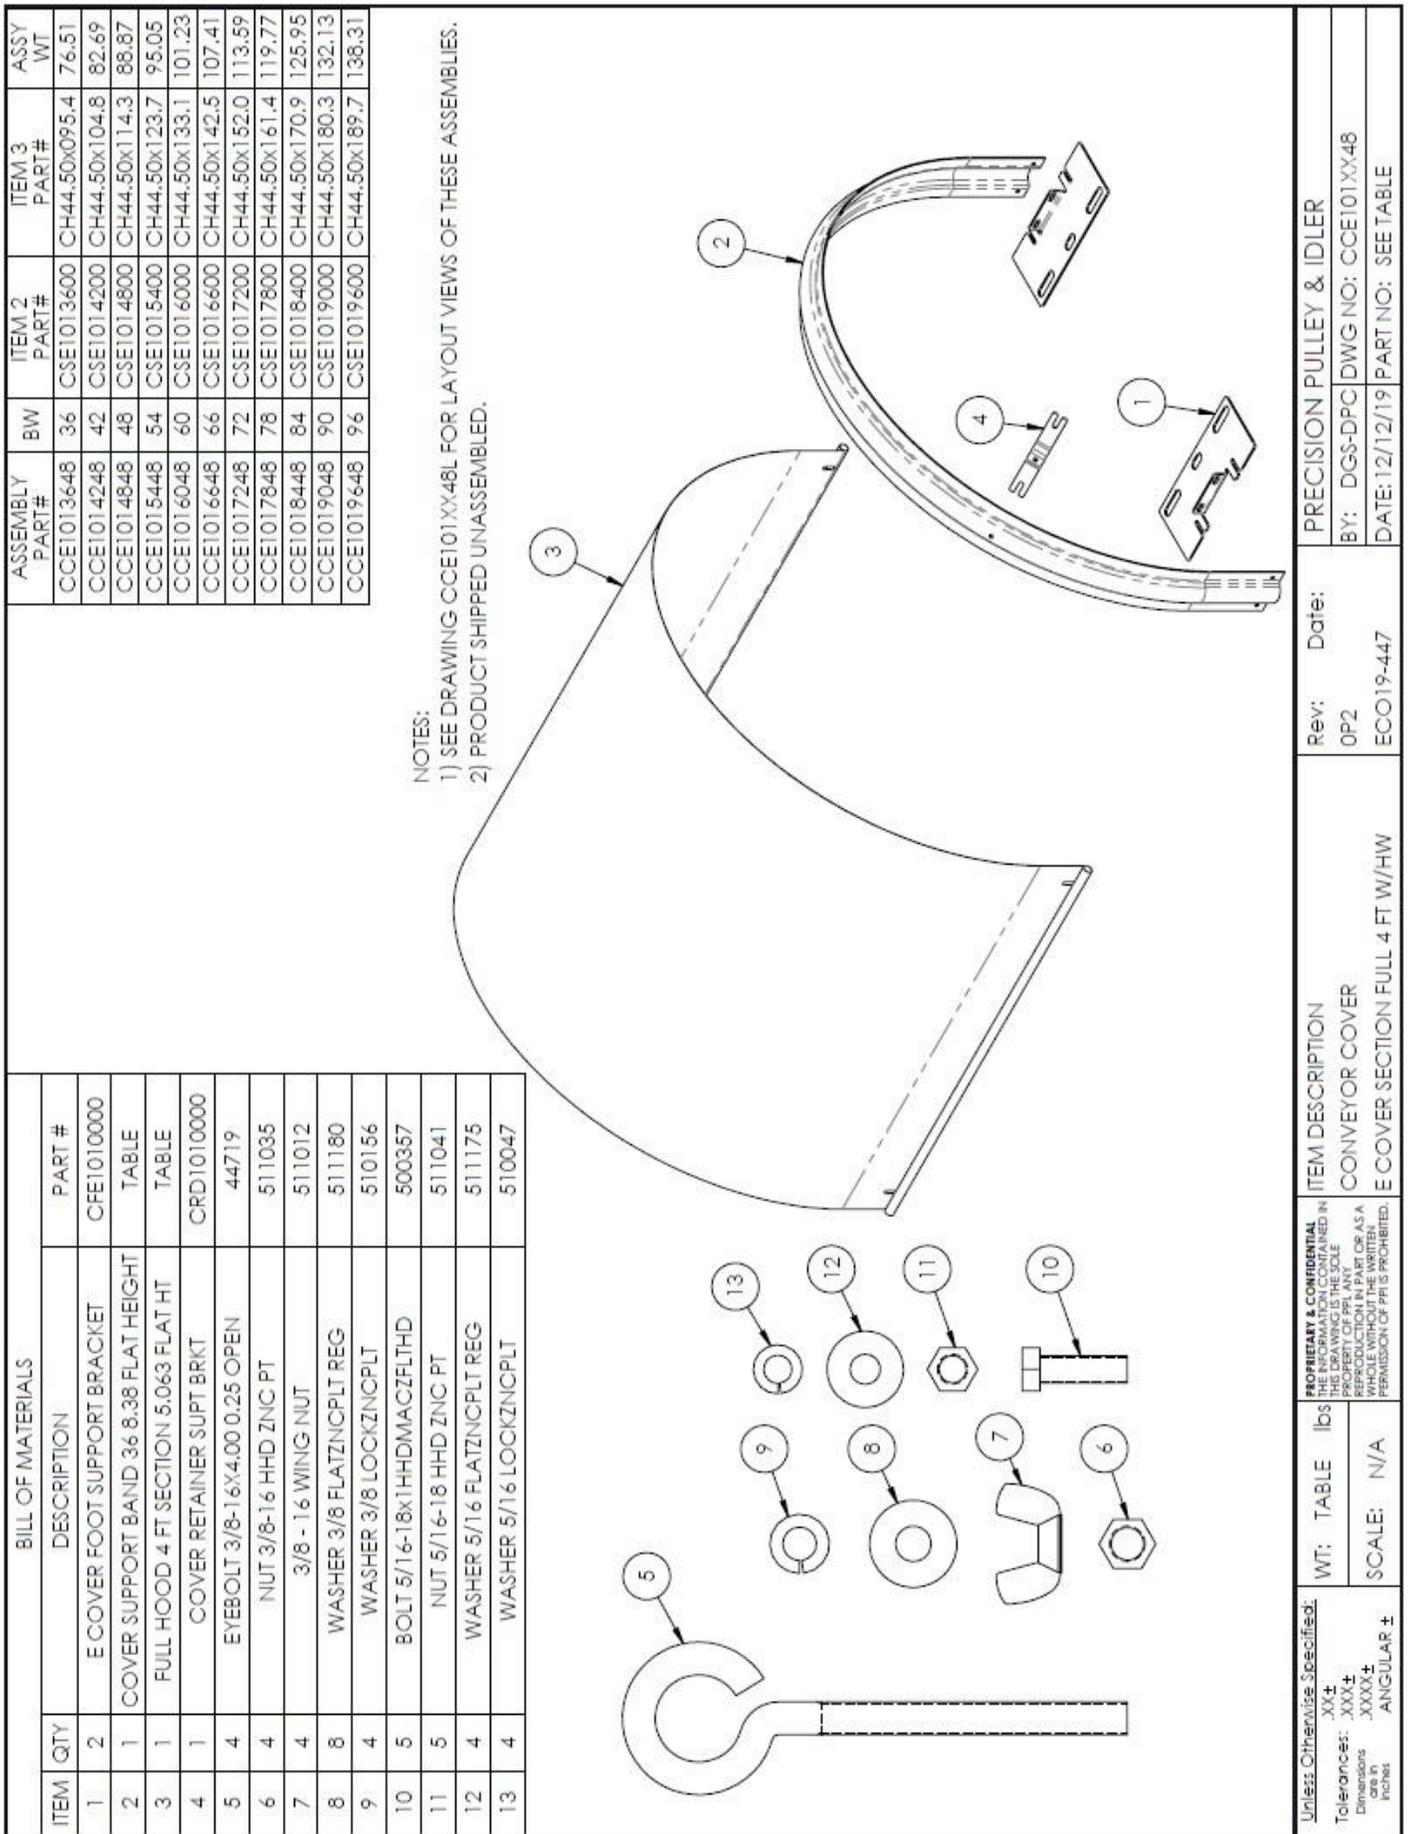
E, SECCIÓN CUBIERTA COMPLETA, 4 PIES CON ELEMENTOS DE SUJECIÓN
